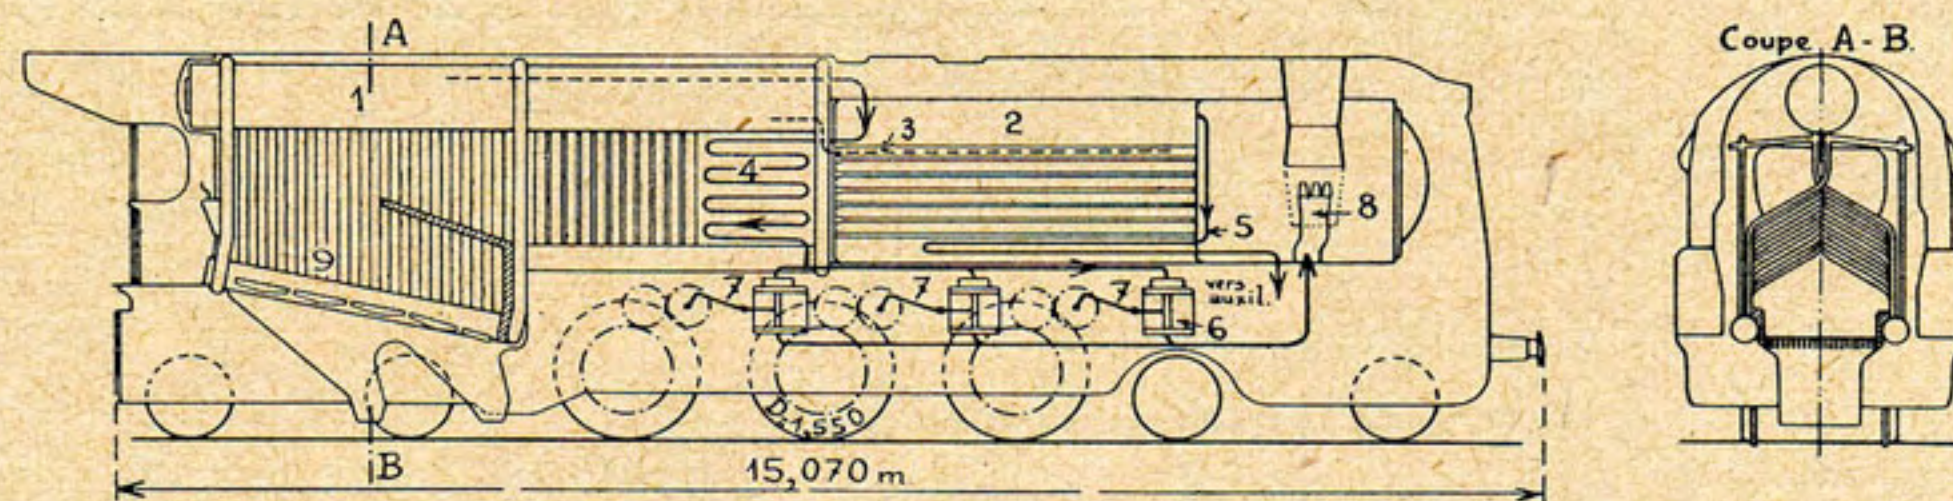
et 164. — Locomotive du type 2—3—2 (*Baltic*) de la S.N.C.F. — Chaudière à tubes d'eau, fournissant de la vapeur à 60 kg. — Attaque de chaque essieu moteur par des moteurs individuels.
